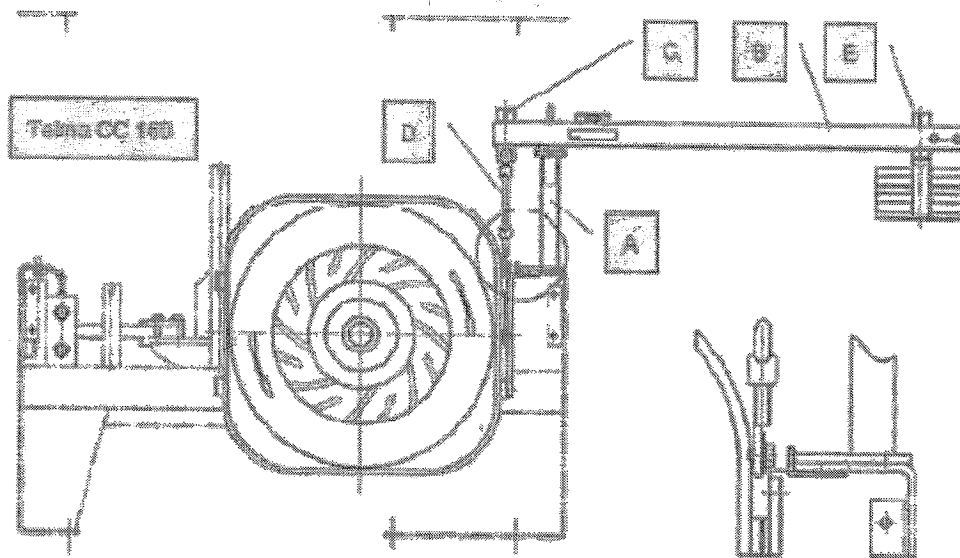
Схема установки калибровочного рычага для модификаций FPS 2700/5500 (А – опора калибровочного рычага; В - калибровочный рычаг; С - кронштейн; D - резьбовая тяга; Е – калибровочные грузы)
